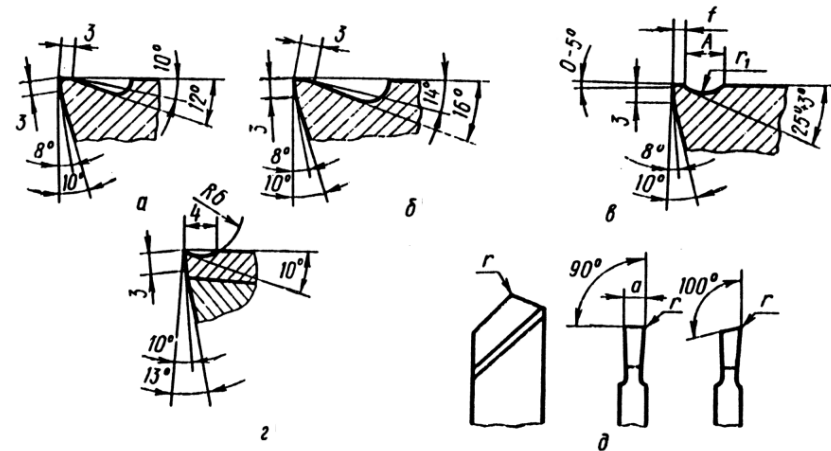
Формы передней поверхности резцов из быстрорежущей стали
